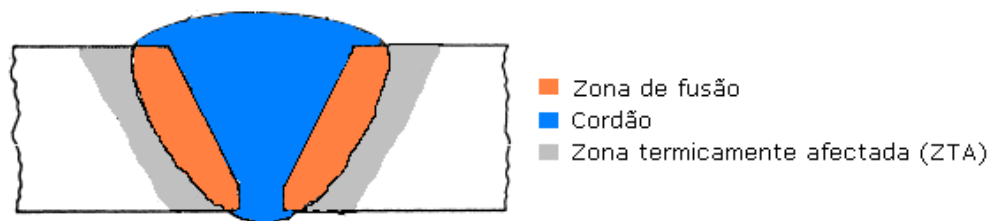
Zonas distintas de uma peça soldada [29].
